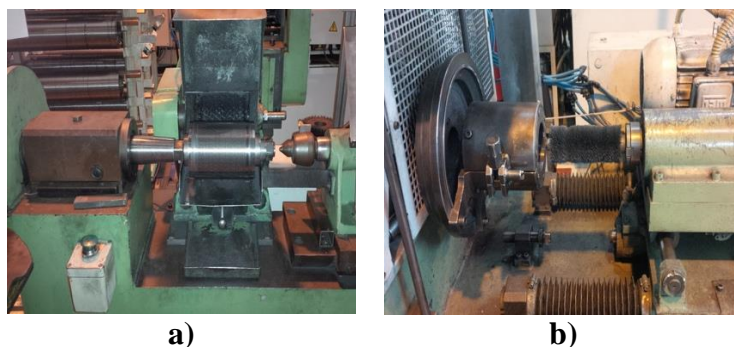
a) Máquina de Escovagem Externa; b) Máquina de Escovagem Interna (MAHLE Componentes de Motores S.A.).
